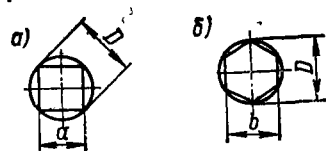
Эскизы для расчета диаметров заготовок под квадрат и шестигранник.
